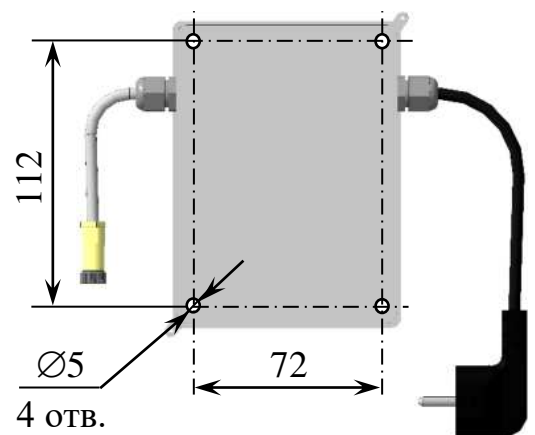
Расположение отверстий для крепления источника питания ИП-1002
